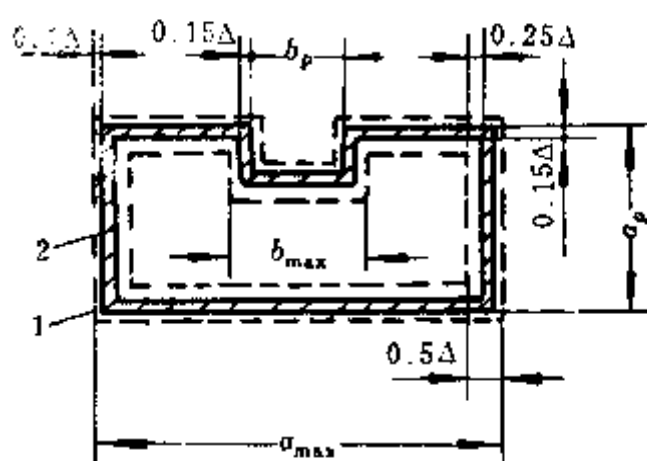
凸模工作尺寸与制件公差的位置
